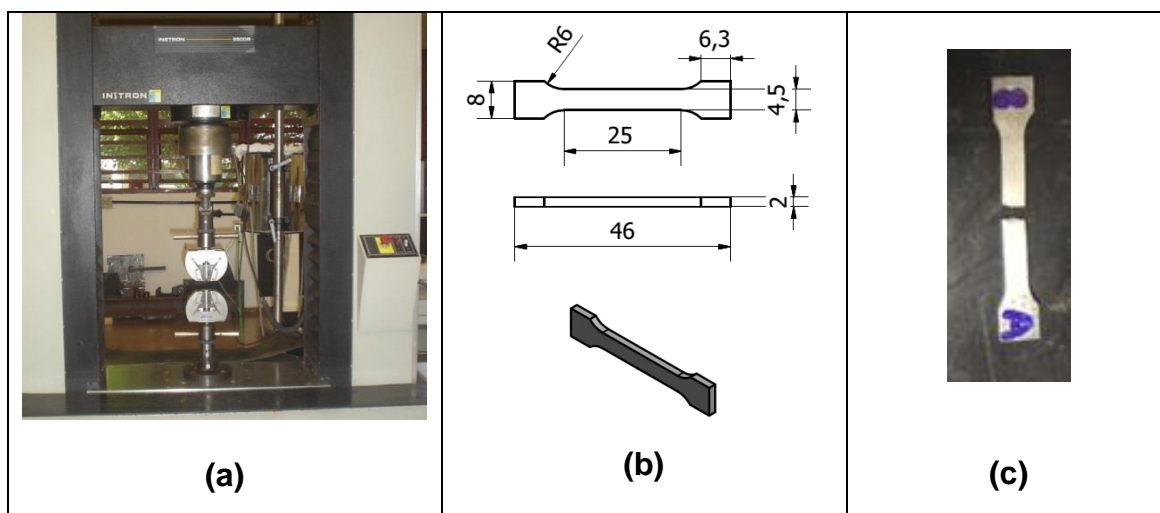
Ensaio de tração: (a) máquina universal de ensaios mecânicos Instron modelo 5500R; (b) Dimensões dos corpos de prova (dimensões: mm); (c) Ruptura do corpo de prova.
